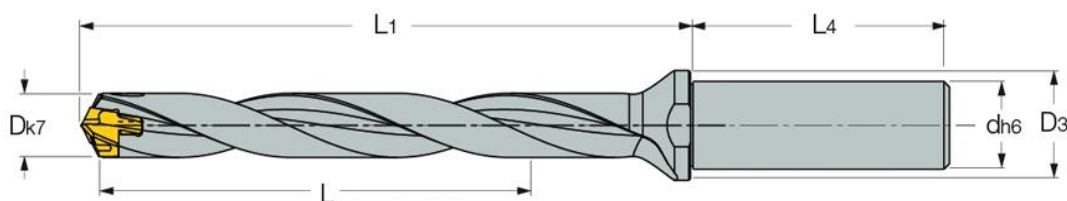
Сверло DCN 060-048-12R-8D
